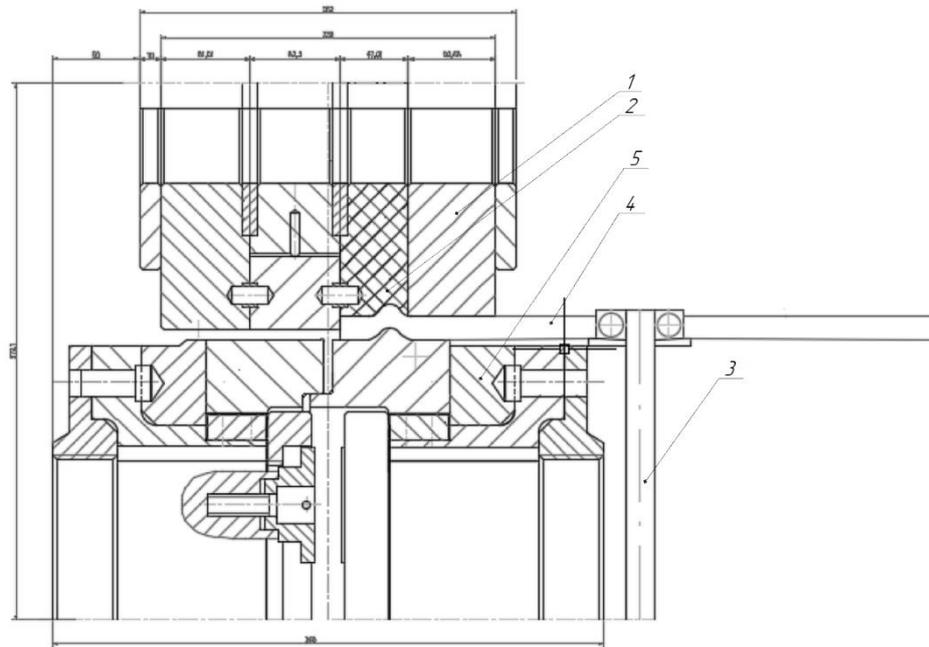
Деформирующие ролики для накатывания профиля: 1 – сборный верхний ролик, 2 – эластичная вставка, 3 – стойка для заготовки диска (удерживающее устройство), 4 – заготовка, 5 – сборный нижний ролик
